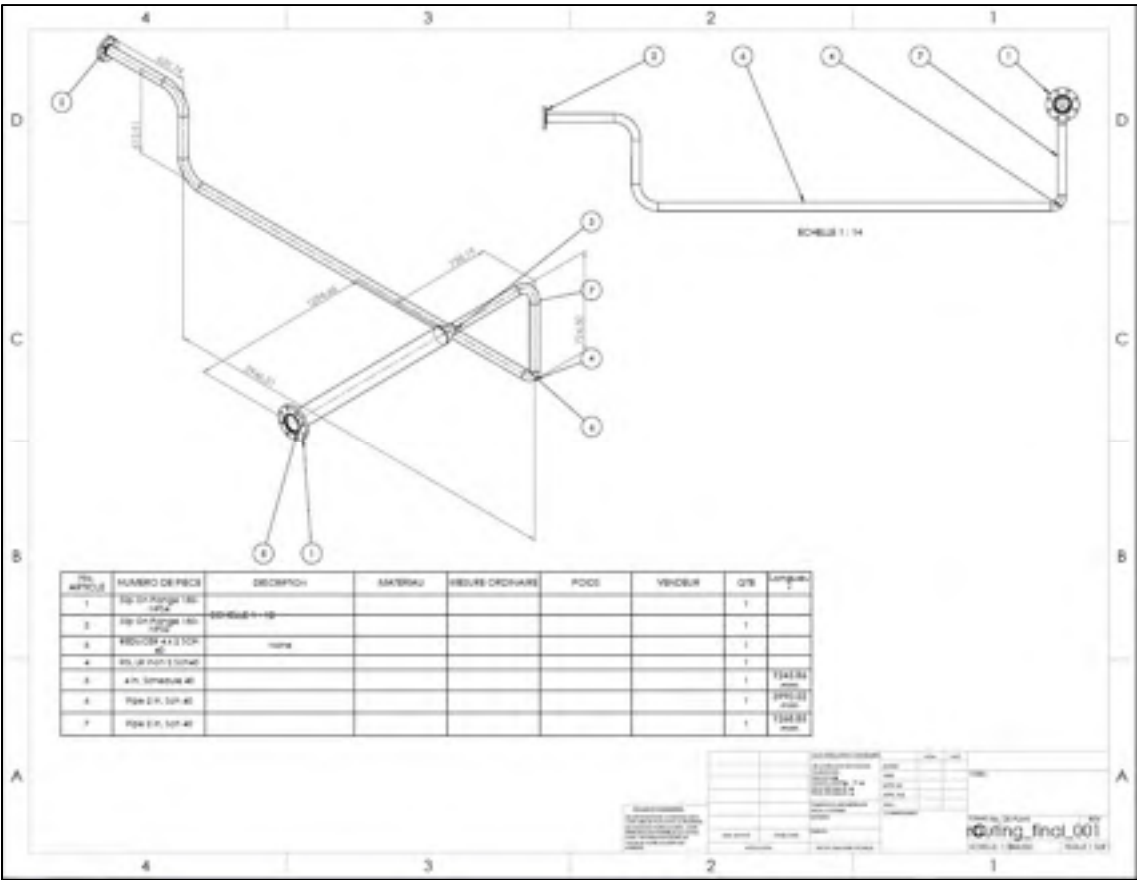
Exemple de mise en plan d'une section de tuyaux
